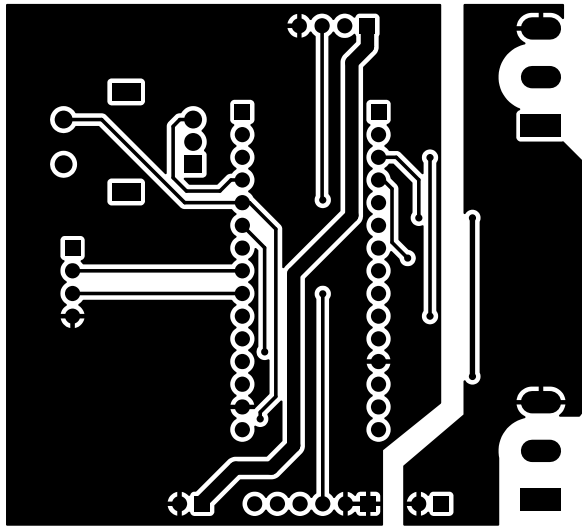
Στιγμιότυπο σχεδίασης PCB
